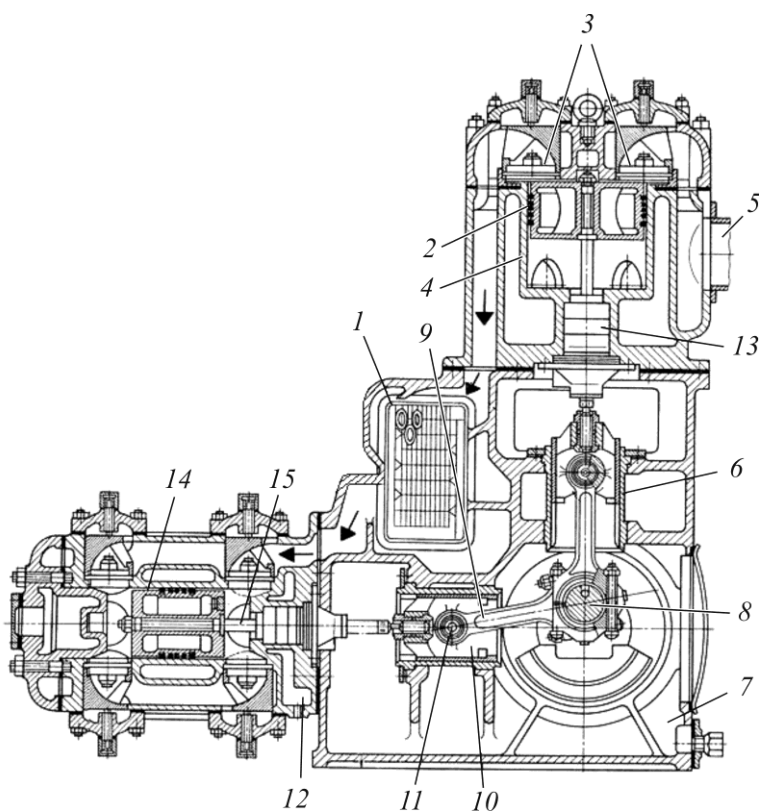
Прямоугольный двухступенчатый поршневой крейцкопфный компрессор: 1 – межступенчатый охладитель газа; 2 – поршень; 3 – клапаны первой ступени; 4 – цилиндр первой ступени; 5 – всасывающий патрубок; 6 – направляющая крейцкопфа; 7 – станина-картер; 8 – коленчатый вал; 9 – шатун; 10 – крейцкопф; 11 – палец крейцкопфа; 12 – нагнетательный патрубок; 13 – уплотнение штока; 14 – поршень второй ступени; 15 – шток
